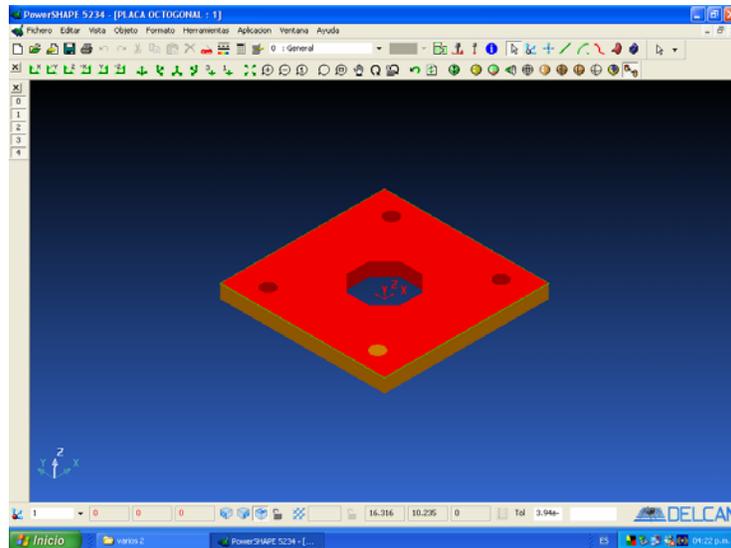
Dibujo del molde octogonal en un programa CAD
